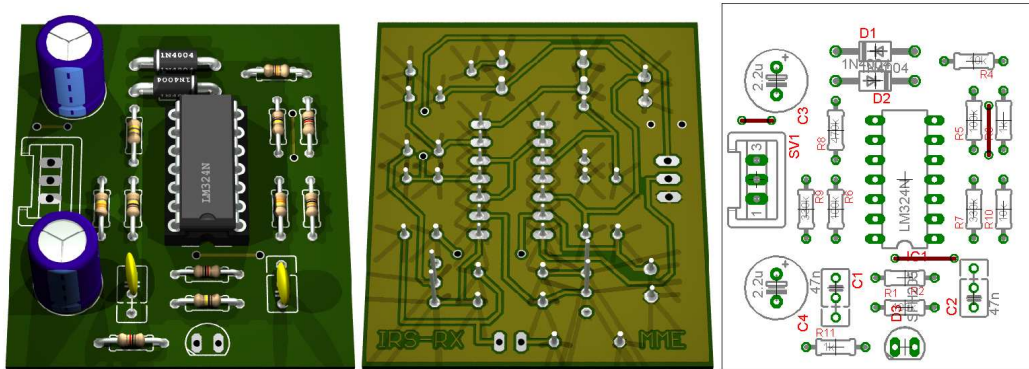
PCB ricevitore lato componenti (sinistra) e lato rame (destra)
